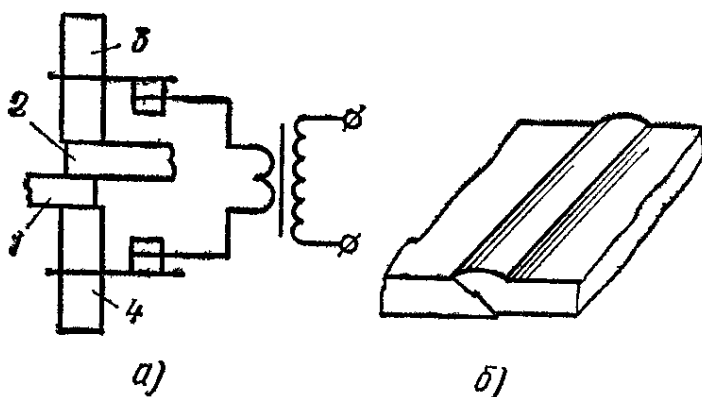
Схема шовно-стыковой сварки (а) и сварной шов (б)
